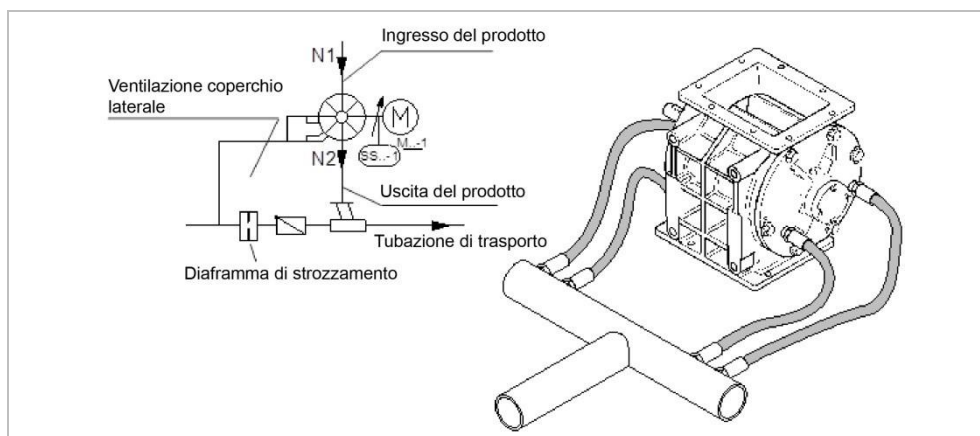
Schema di collegamento ventilazione coperchio laterale
